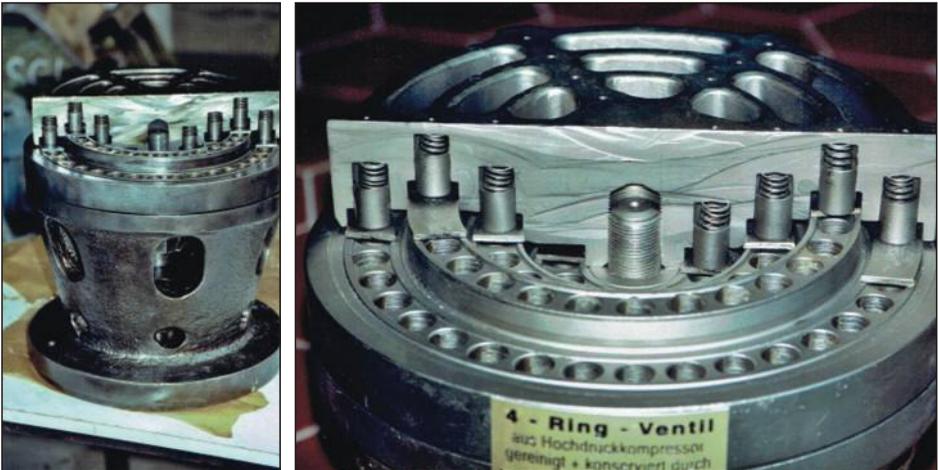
a,b Hörbigerventil a) komplettes Ventil mit halbgeöffneter Platte b) Detailansicht
